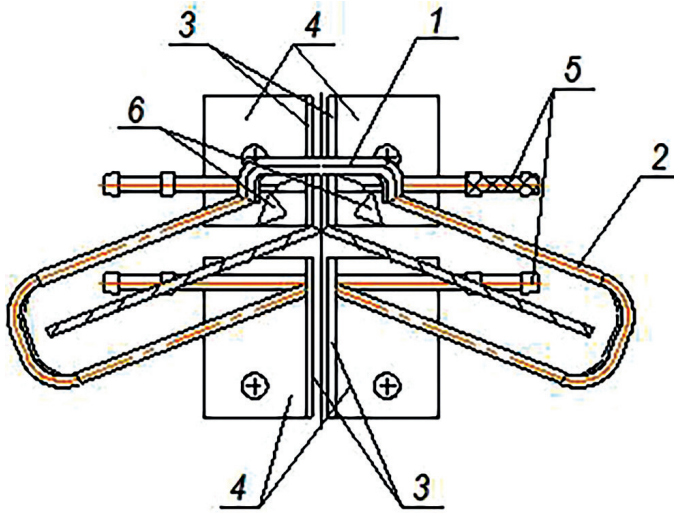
Индуктор для одновременной наплавки носовой части стрелчатой лапы и закалки ее крыльев: 1, 2 – наплавочный и закалочный виток; 3 – токопровод; 4 – пластина для присоединения к генератору; 5 – штуцер; 6 – профилированная трубка для плавления шихты
